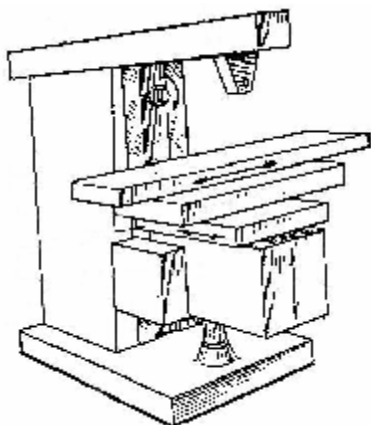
Компоновка консольного горизонтально-фрезерного станка
